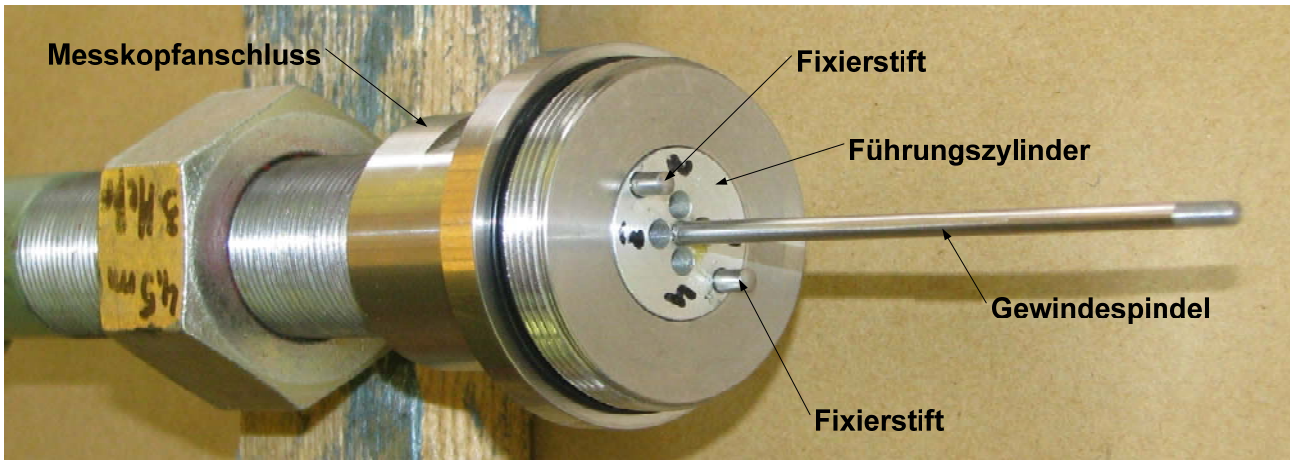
Messkopfanschluss mit Führungszylinder und Gewindespindel vor der Montage
